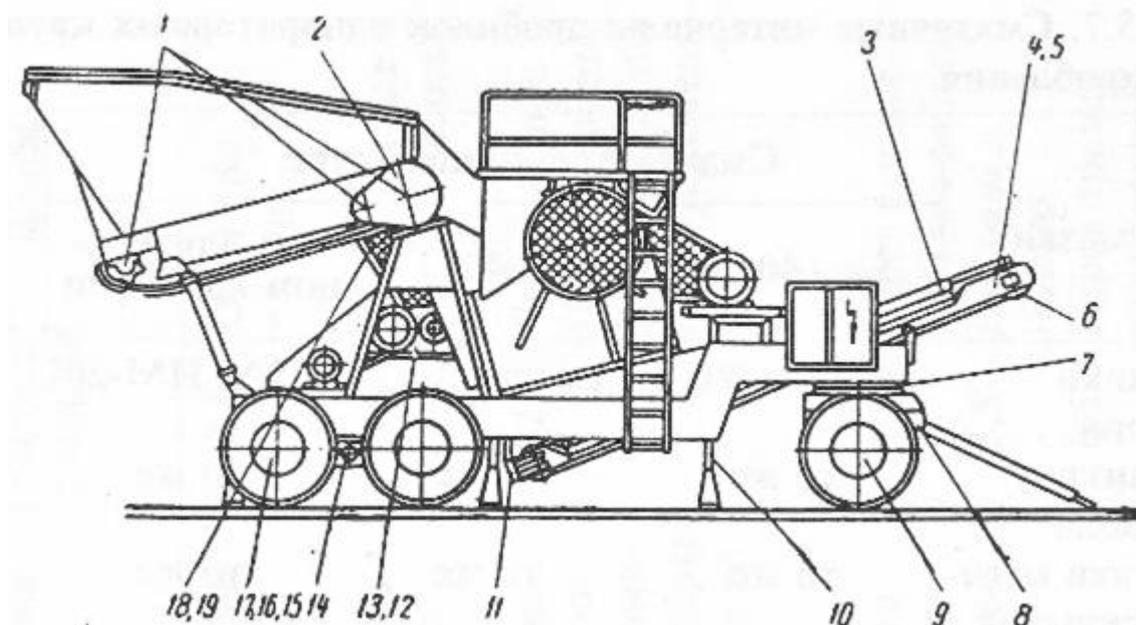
Схема смазки передвижного агрегата среднего дробления: 1 — валы питателя; 2 — зубчатые колеса привода питателя; 3 — ролики конвейера; 4, 5 — редуктор конвейера; 6 — барабаны конвейера; 7, 8 — тележка передняя; 9 — колесо тележки; 10 — домкрат; 11 — натяжное устройство; 12, 13 — редуктор питателя; 14—17 задняя тележка; 18, 19 — привод питателя
